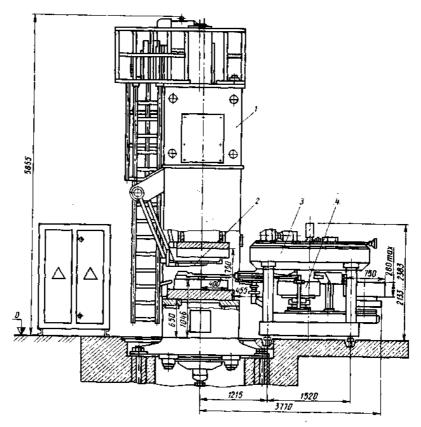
Автоматизированный комплекс для штамповки деталей из штучных заготовок (модель АКК3535А-1)
